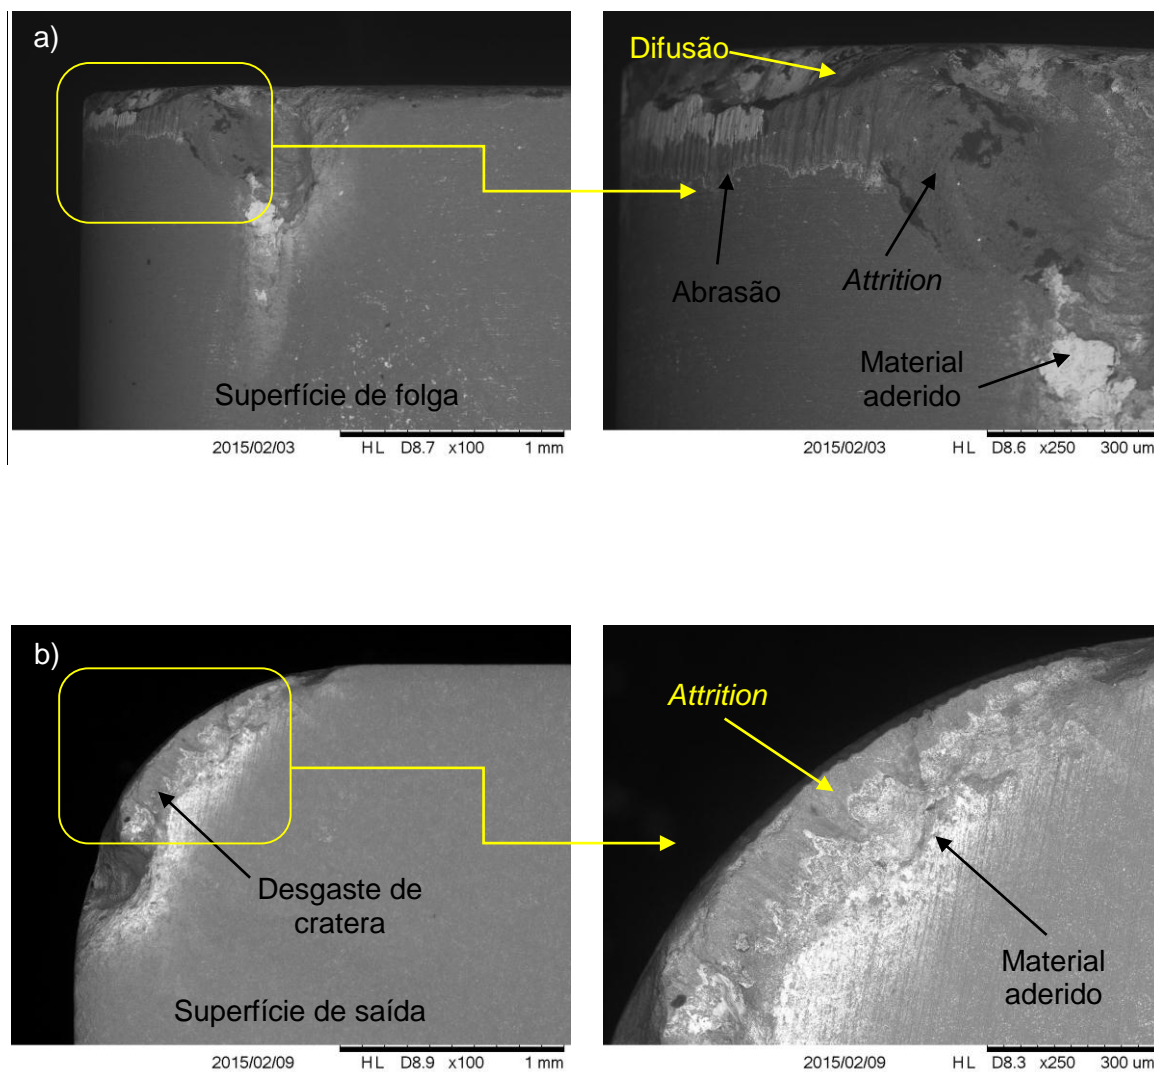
Fotografias obtidas através do MEV das ferramentas *whisker* após a usinagem do Inconel 718 com aplicação de fluido de corte LB 2000 por MQF. (a) superfície de folga e (b) superfície de saída
